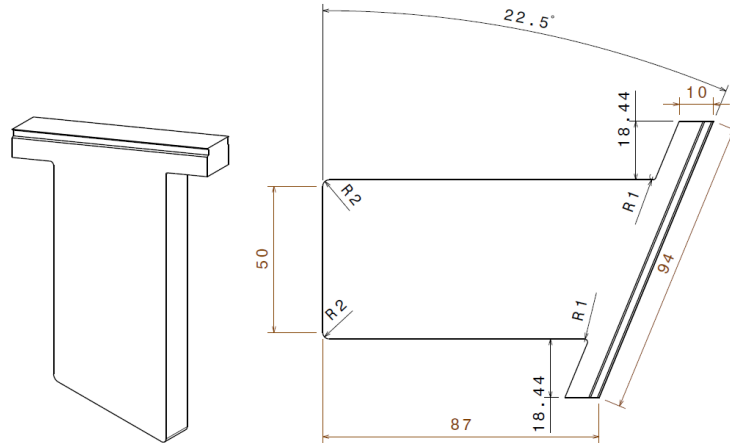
Plan d'usinage de l'éprouvette Scarf modifié 22.5°.
